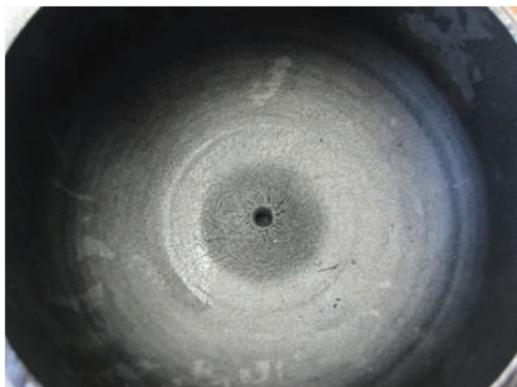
Возможный дефект в глухом днище баллона, изготовленного из трубной заготовки
